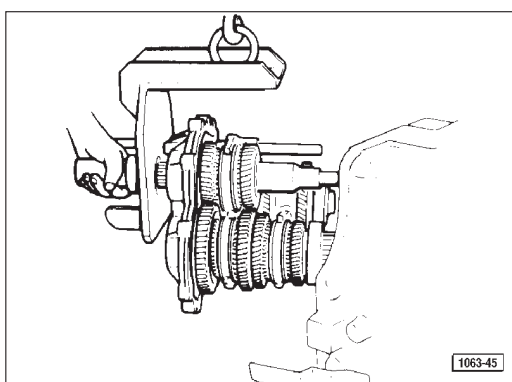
Démontage de l'ensemble des pignons des vitesses de la boîte.
